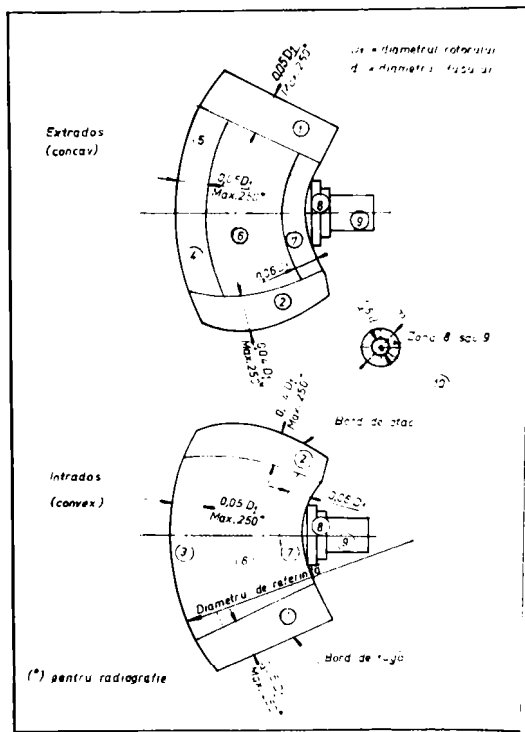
Zone de inspecție pentru palete de rotoare Kaplan [154].
